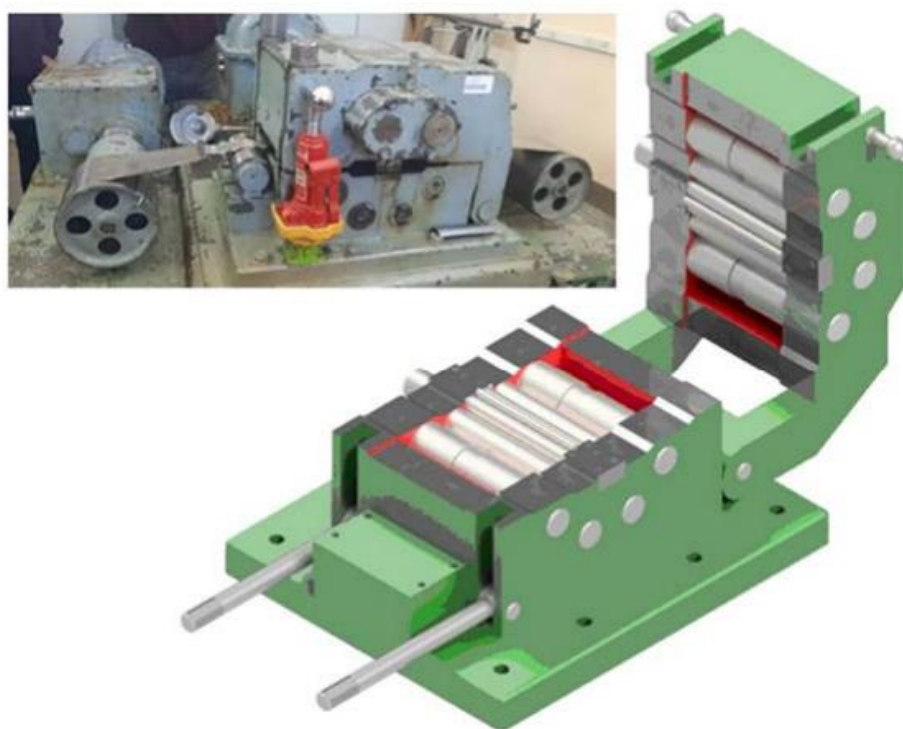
Внешний вид и 3D-модель раскрытой прокатной клетки 20-валкового стана 12/160
